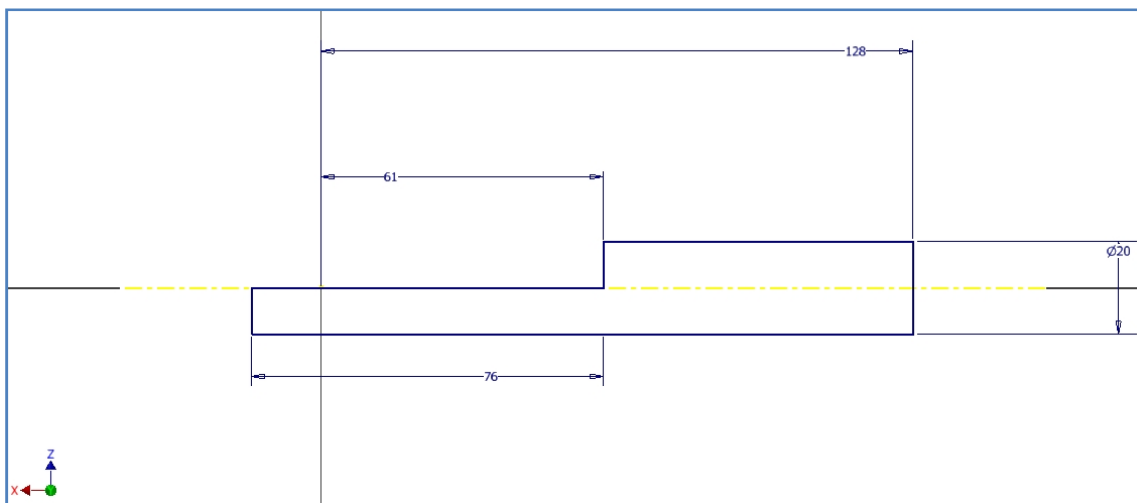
Primer boceto para la primera extrusión de la sección B.
